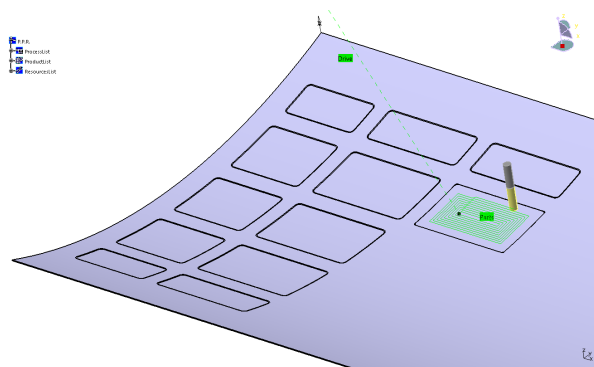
Gewichtsoptimierung durch mechanisches Fräsen von Pockets
